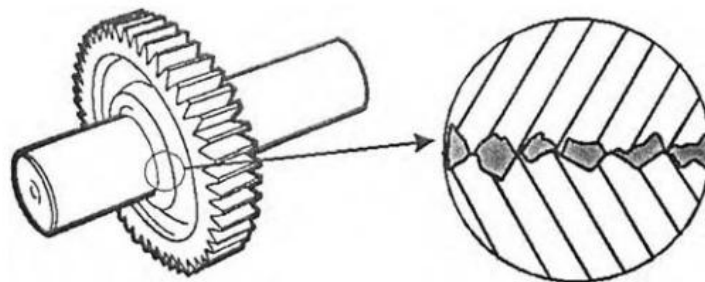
Colagem de engrenagem em eixo (Timings, 2006)
